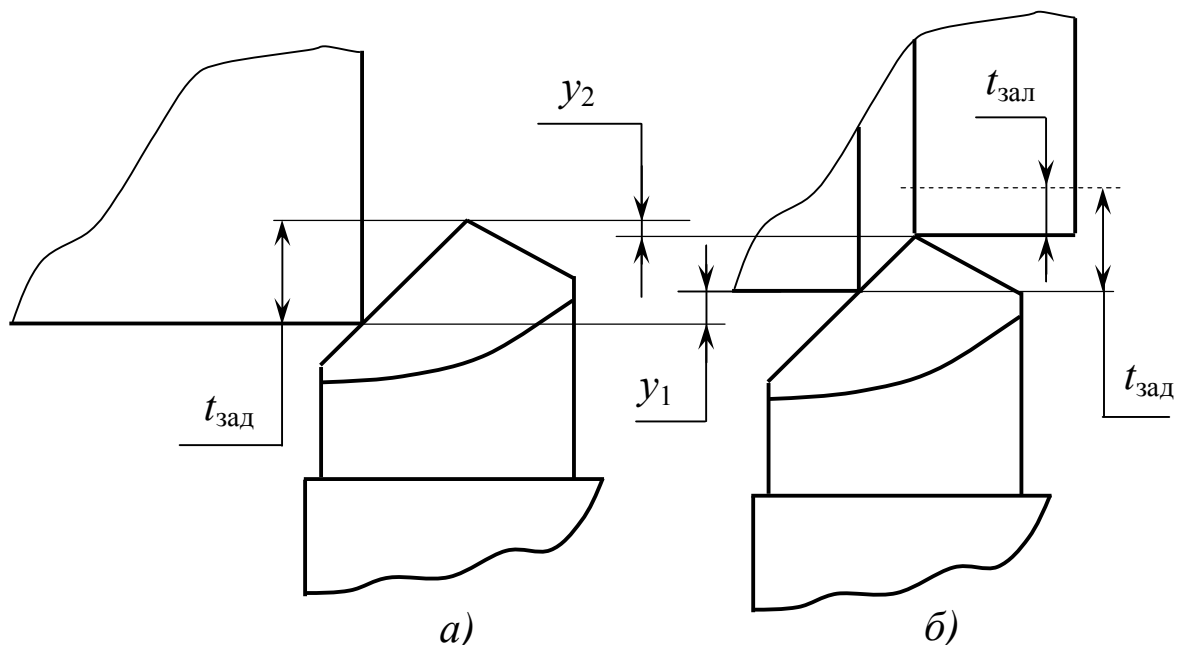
Схема пружних зміщень елементів системи ВПД під час механічної обробки
